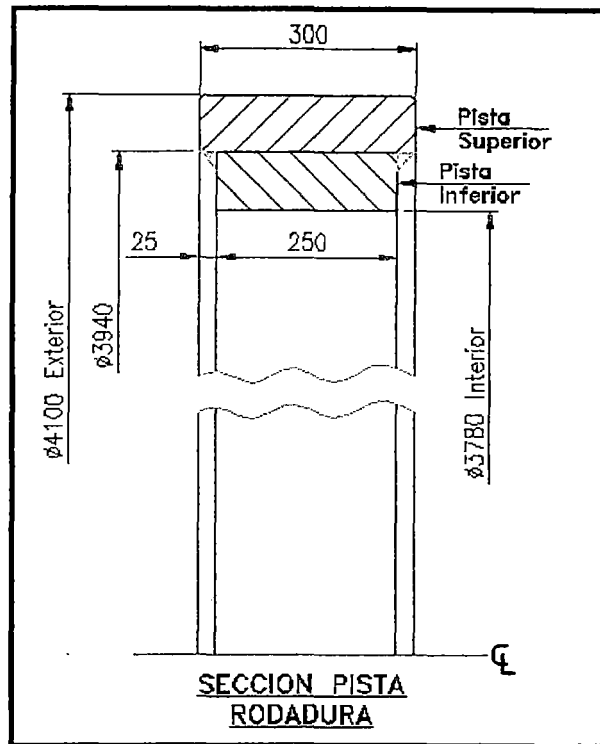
"Dimensionamiento de Pista Rodadura"
